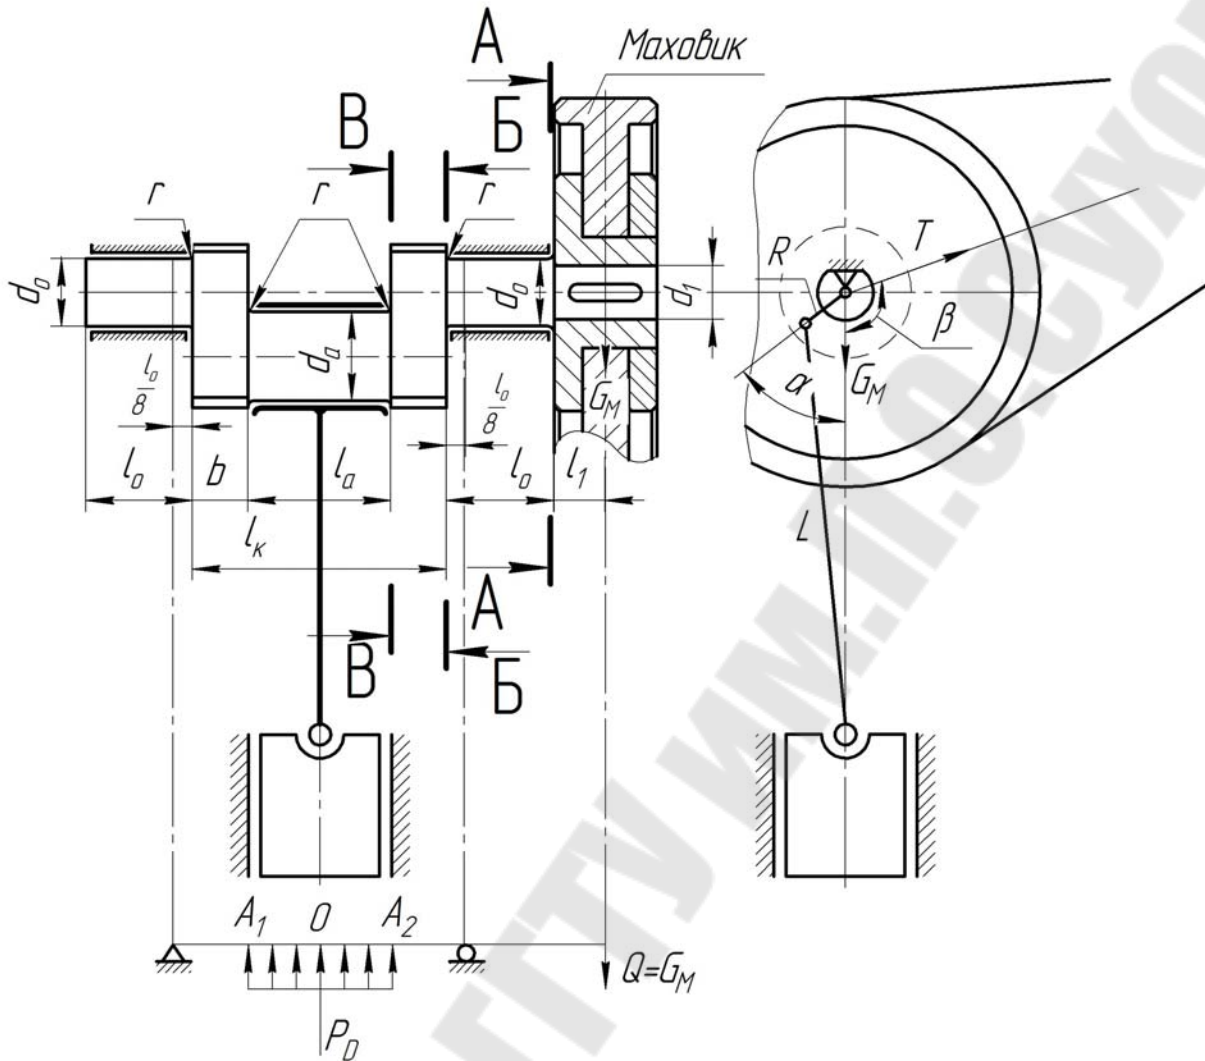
Одноколенчатый вал с маховиком (без зубчатой передачи)
